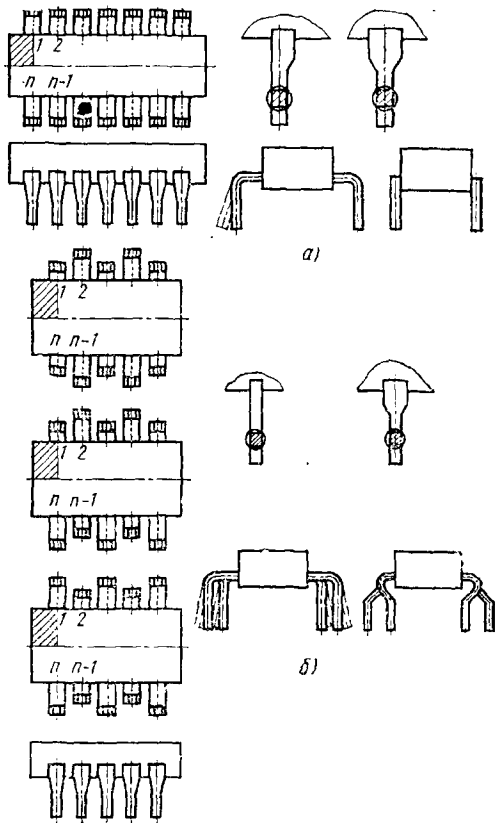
Конструкции корпусов типа 2 подтипов 21(а) и 22(б) с вариантами формовки и конструкций выводов
